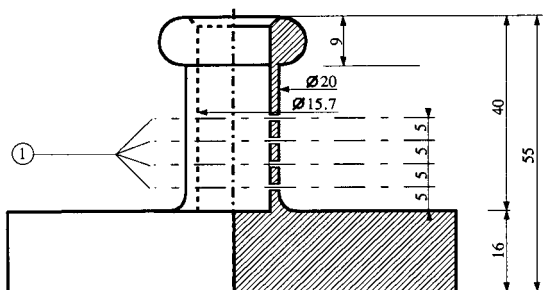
Полый бронзовый цилиндр, закрытый с одной стороны; чертеж и размеры детали в мм
